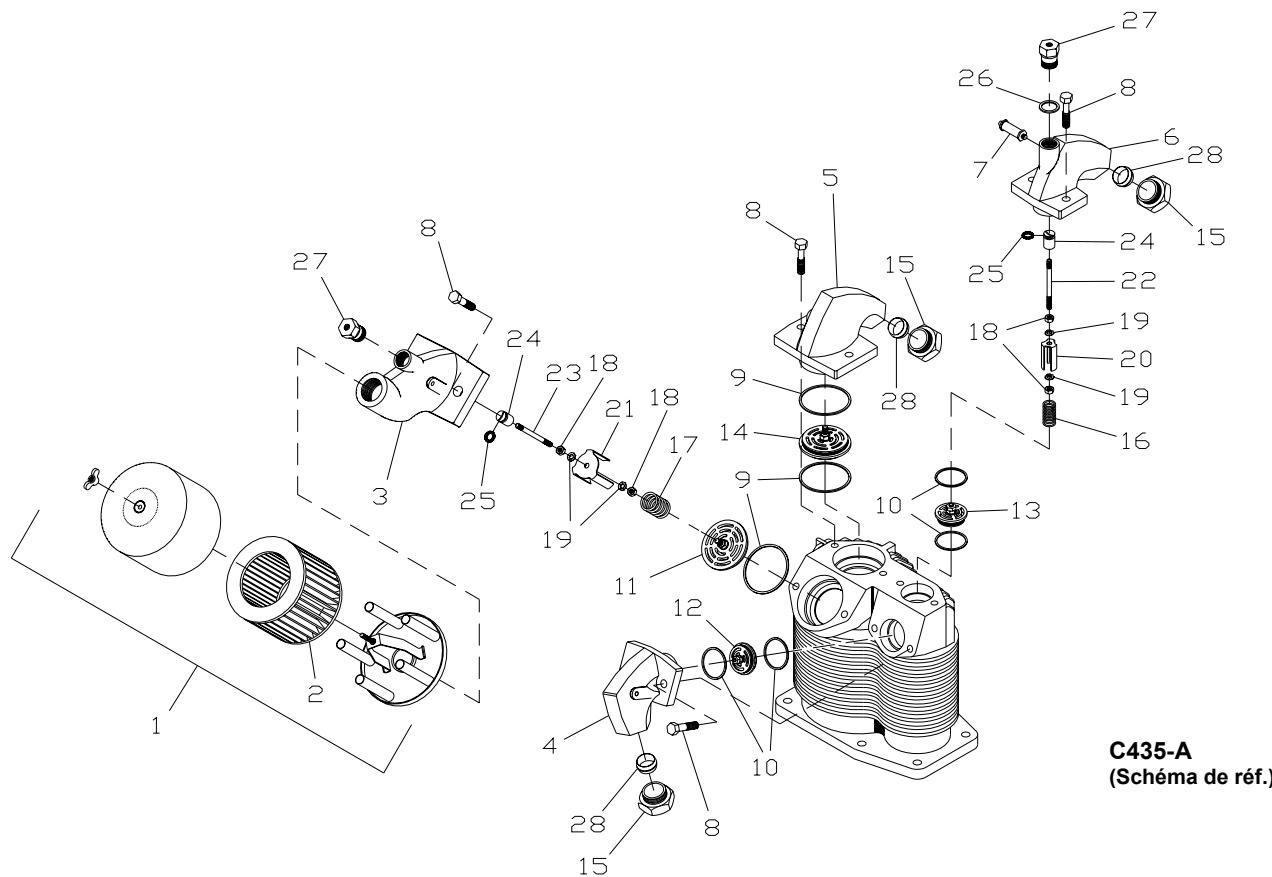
Illustration des pièces de rechange pour l'ensemble de soupape et les collecteurs
